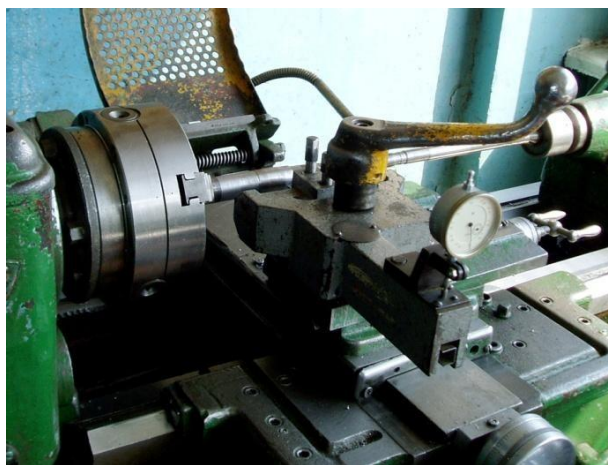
Загальний вигляд пристрою для вимірювання сил різання при точінні покриттів на токарно-гвинторізному верстаті 1А616
